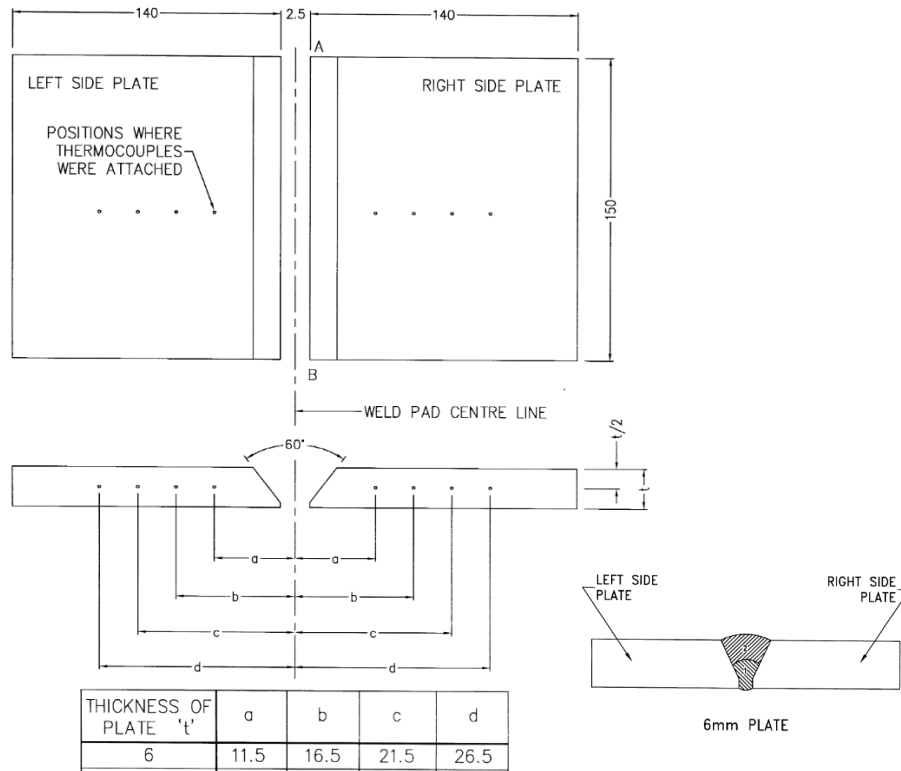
Dimensions (en mm) de l'assemblage de Murugan et al [I.30] et position des thermocouples
